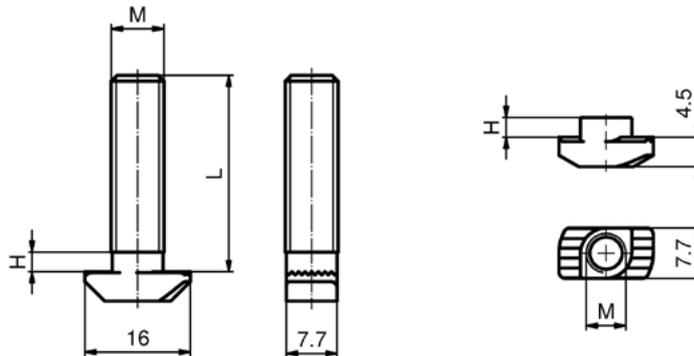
Abmessungen Hammerschrauben und Hammermuttern AXF
